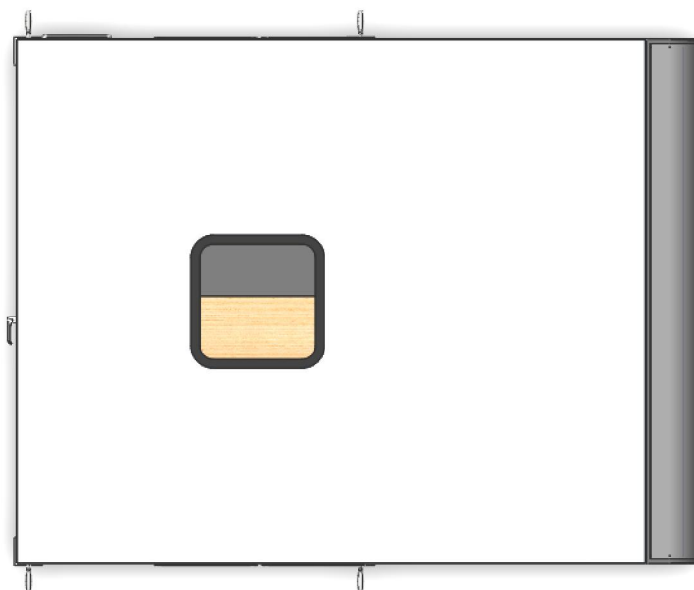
Parte superior de la célula con la escotilla instalada (Fuente: SolidWorks)
